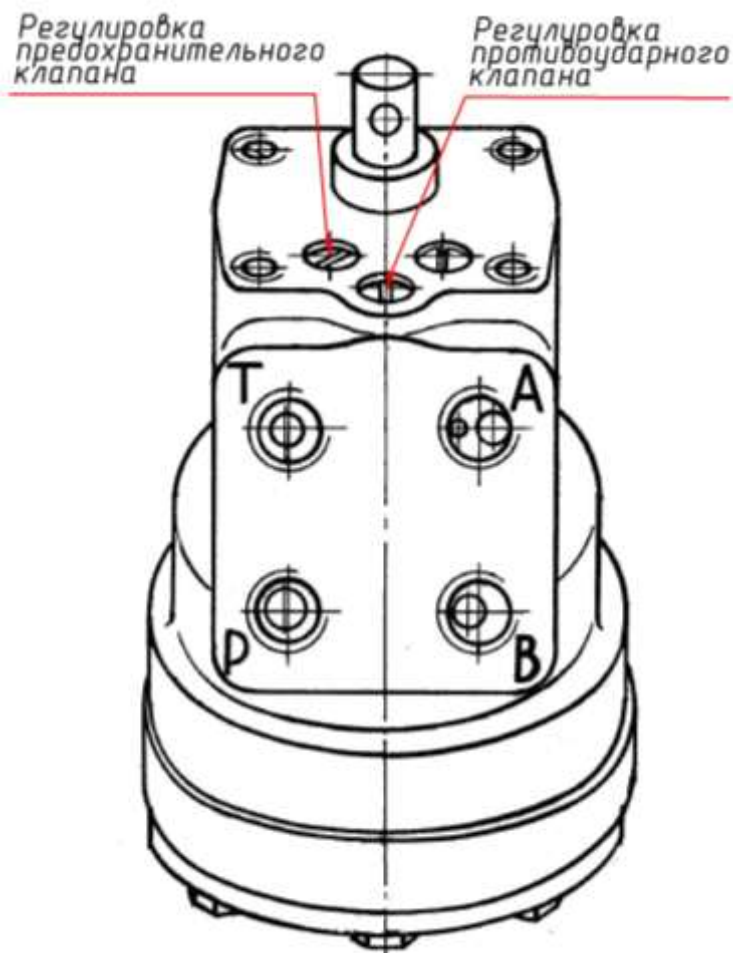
Гидравлический рулевой механизм. Присоединительные отверстия: P - напор; T - слив; A, B - рабочие отводы, соединенные с гидроцилиндром поворота колес.
